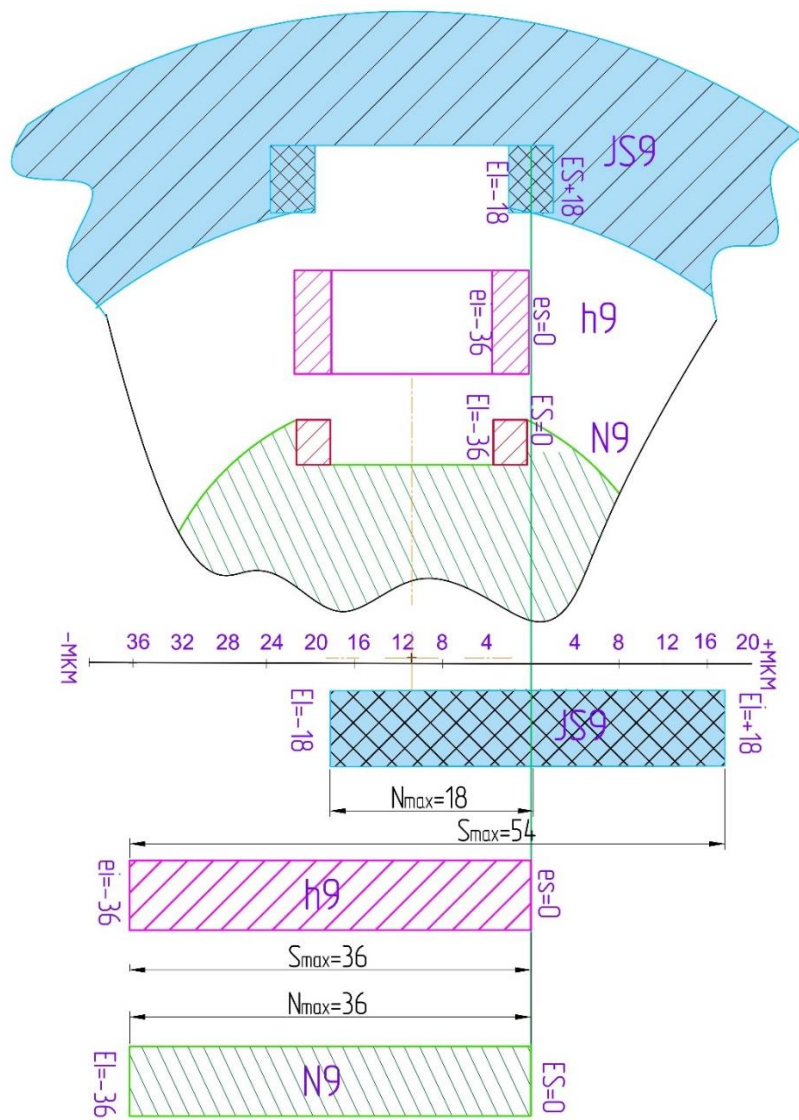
Схема розташування полів допусків для з'єднання
